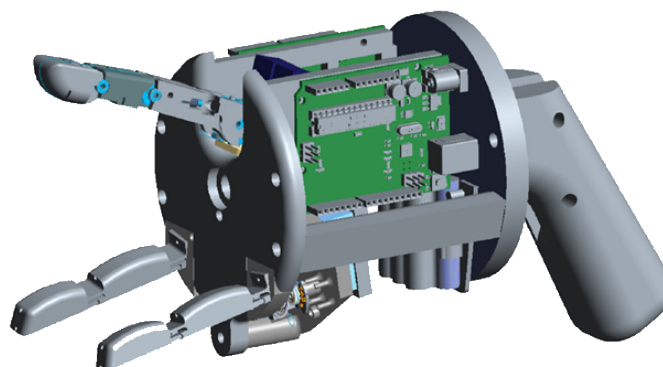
CAD-Zeichnung der WHISG Hand in der Ausführung mit Pistolengriff
